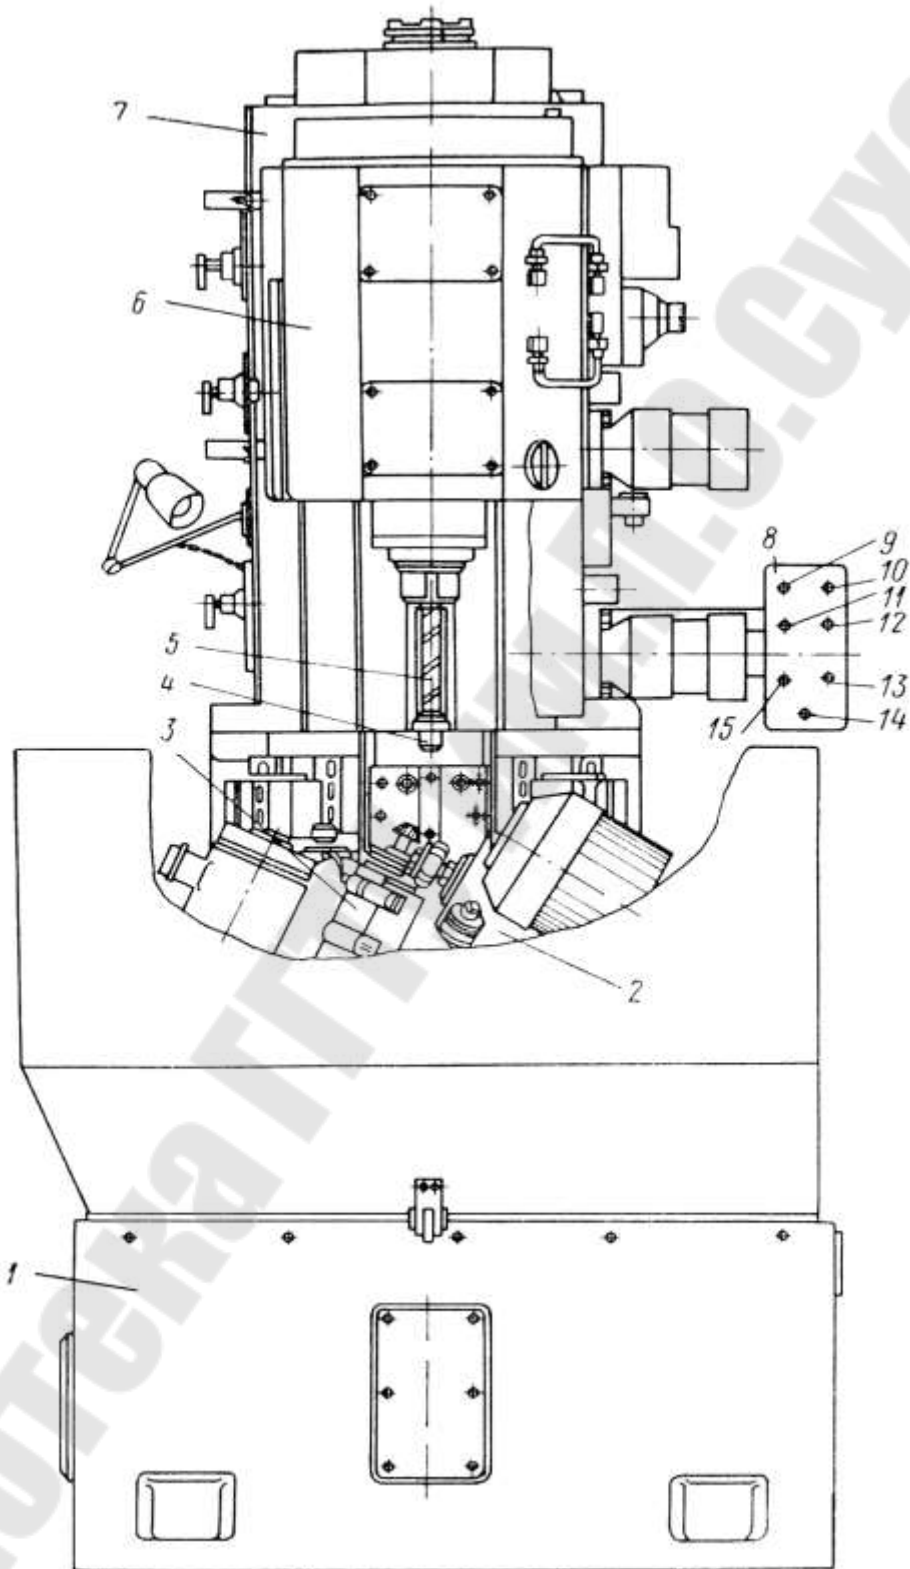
Эскиз общего вида специального сверлофрезерного полуавтомата модели 6В-4М:
